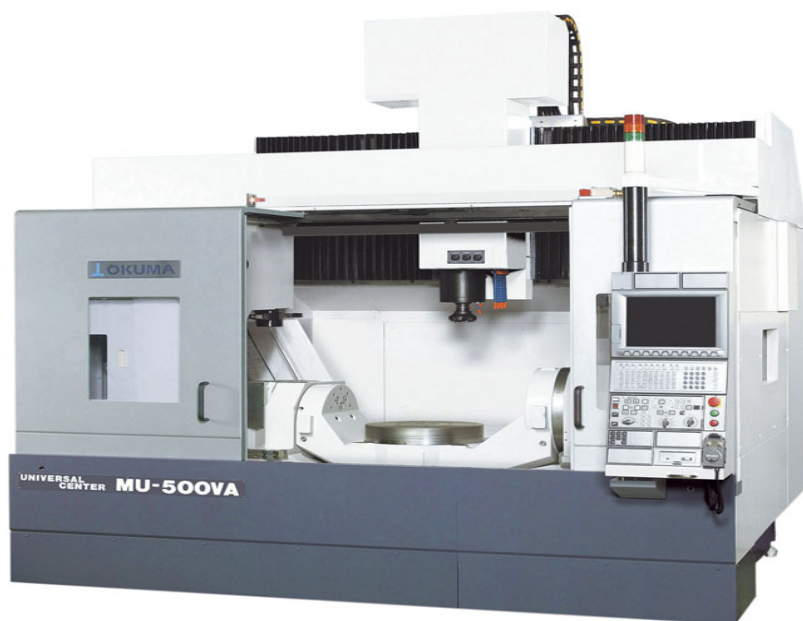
Обрабатывающий центр с ЧПУ модели MU-500VA-L
